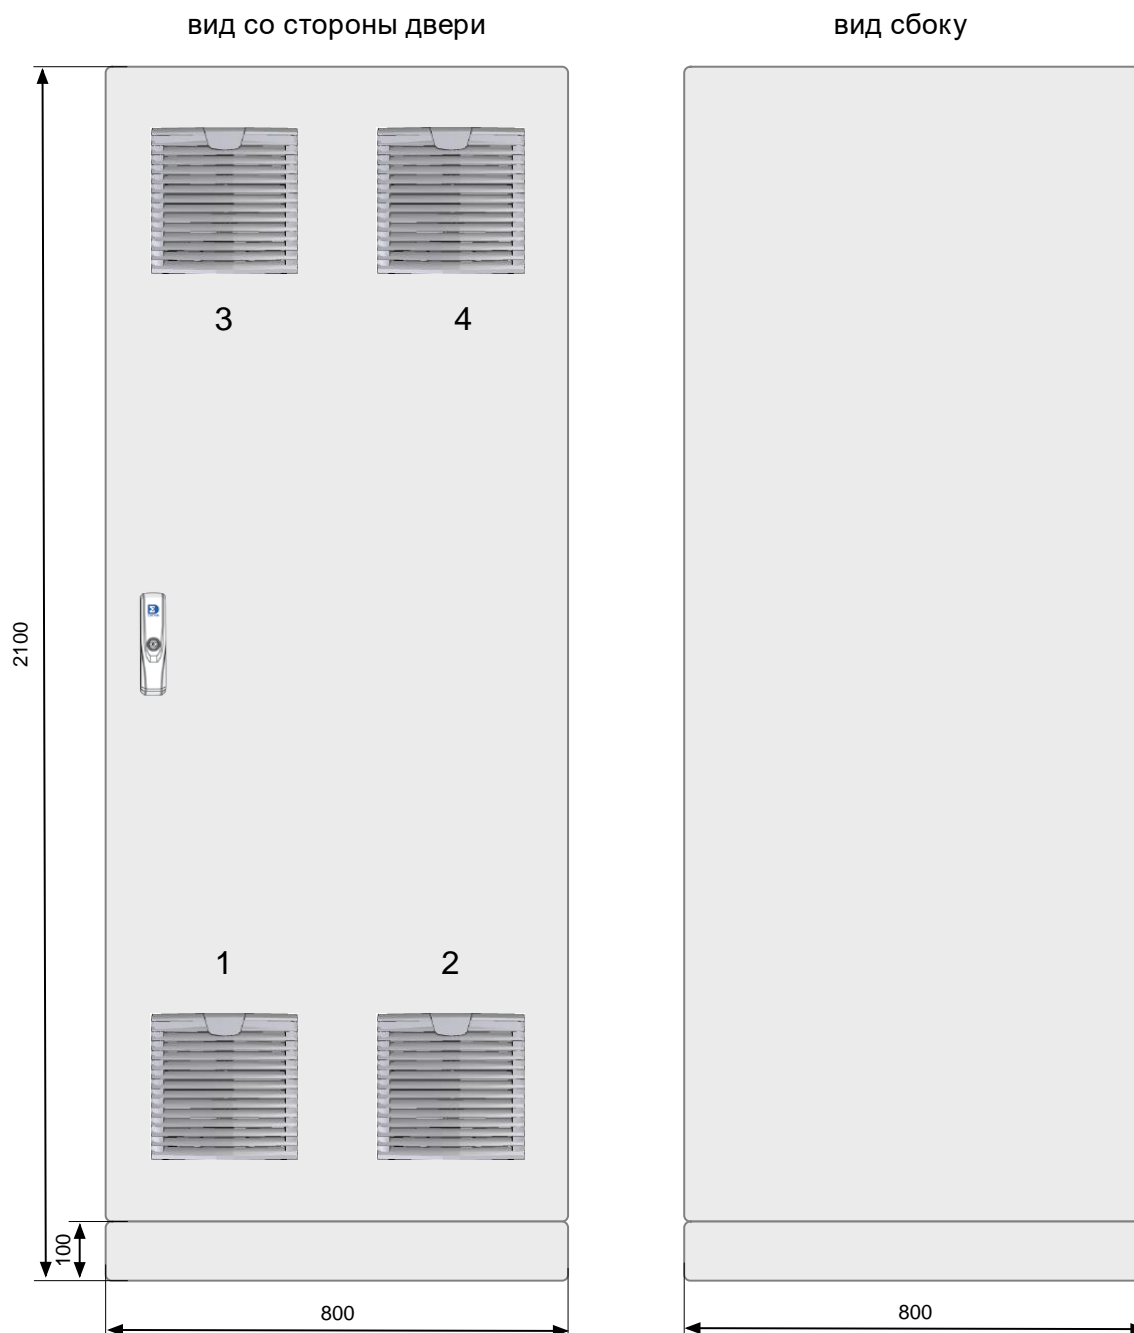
Внешний вид и габаритные размеры концентратора с одностворчатыми дверями
